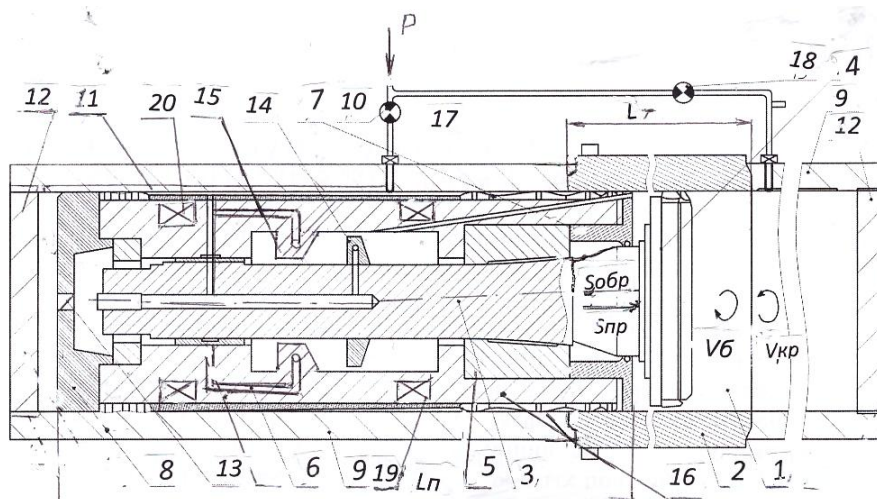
Малогабаритный станок с режуще-деформирующей пинолью для вихрефрезерования или внутреннего шлифования методом винтовой интерполяции
